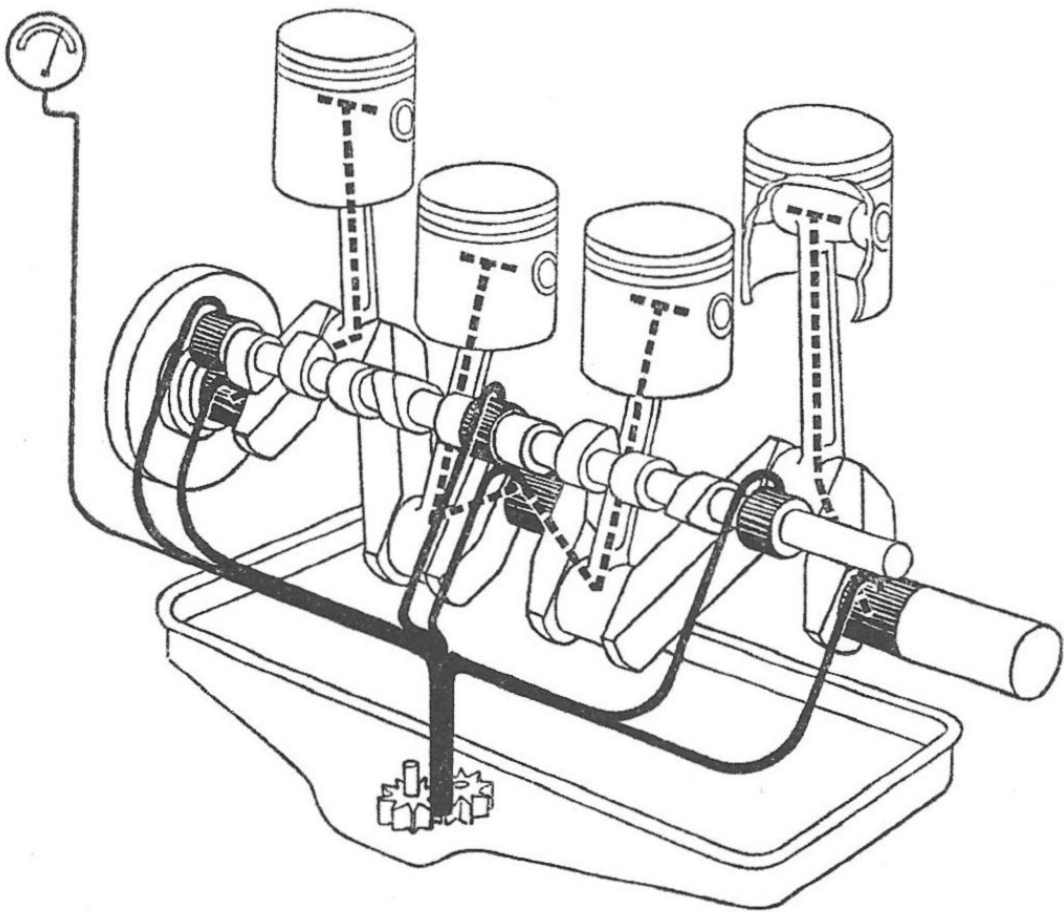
Druck-Umlaufschmierung mit Zahnrad-Ölpumpe und Ölmanometer.
